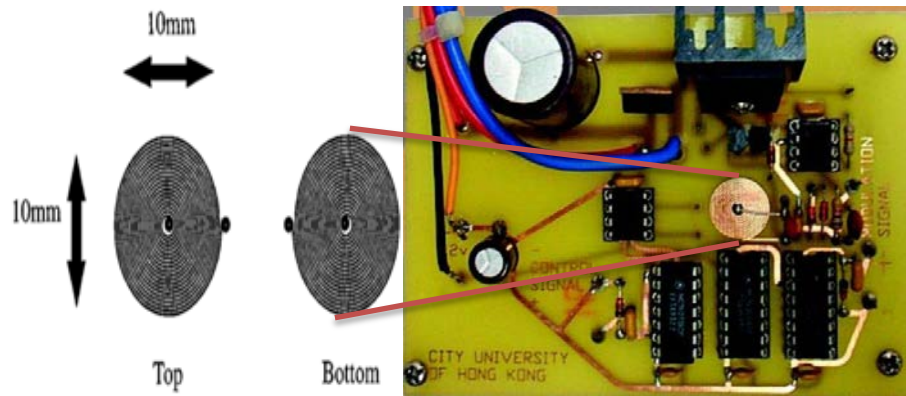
Micro-transformateur PCB sans matériau magnétique [TaHC00]
